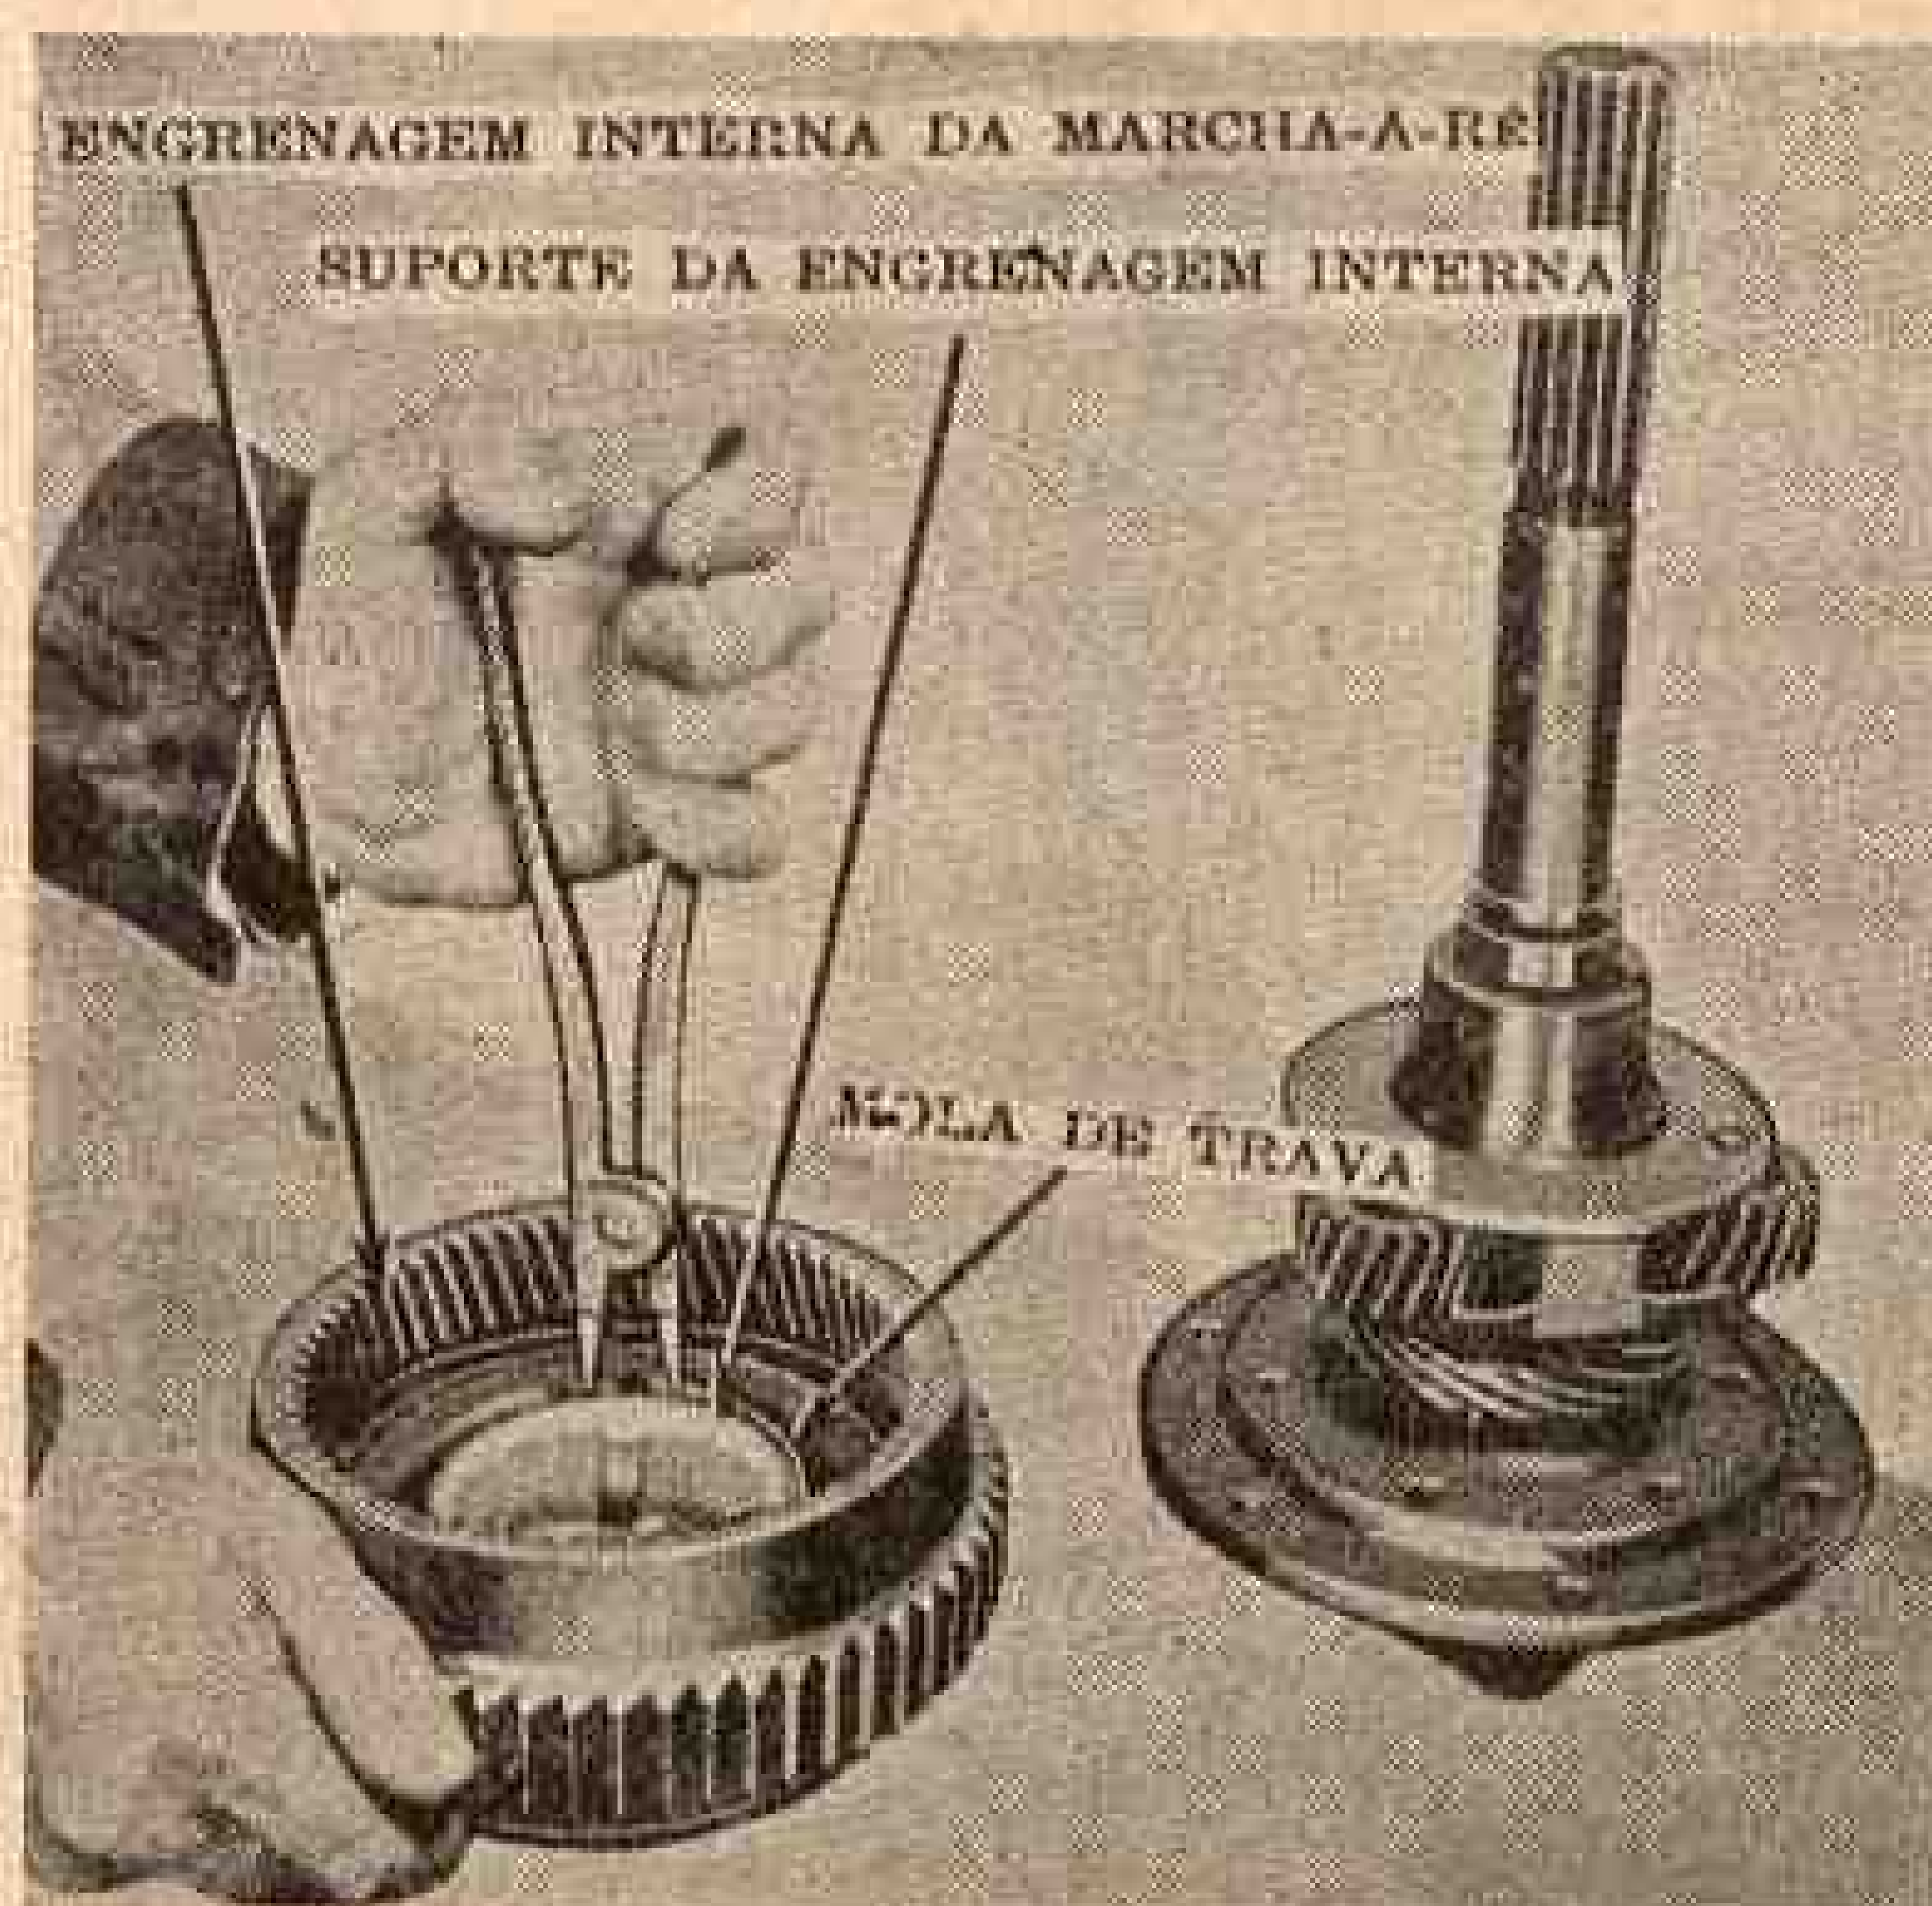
Montando a engrenagem interna de marcha-à-ré
